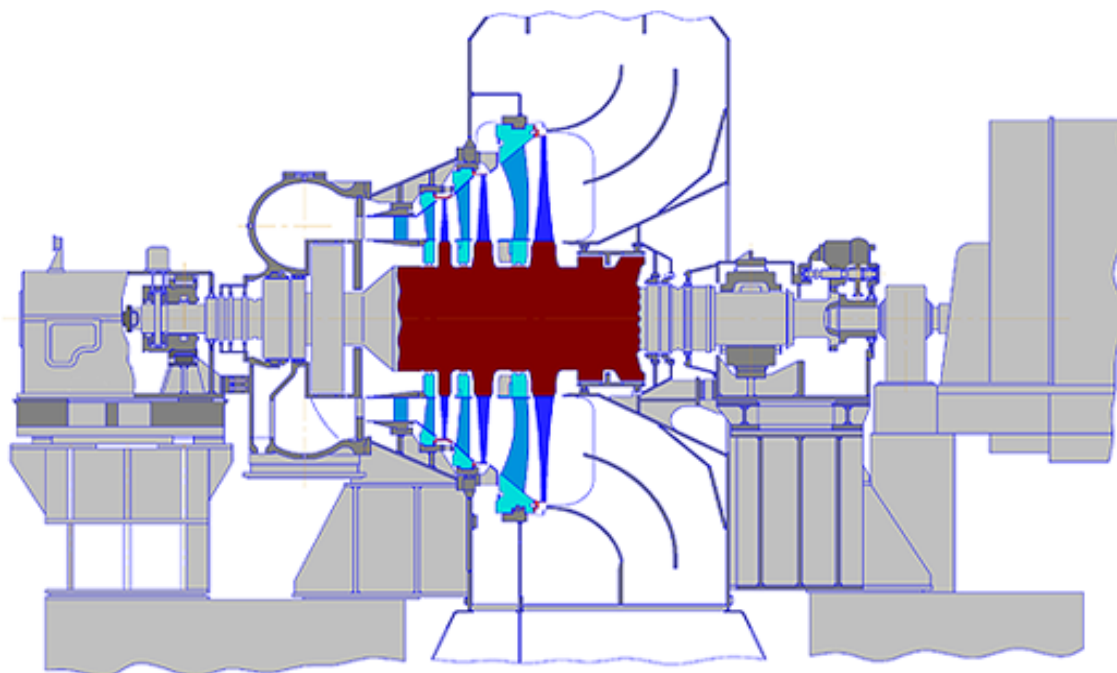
Продольный разрез ЦНД Натурного стенда ЛМЗ с рабочей лопаткой длиной 1400 мм.
